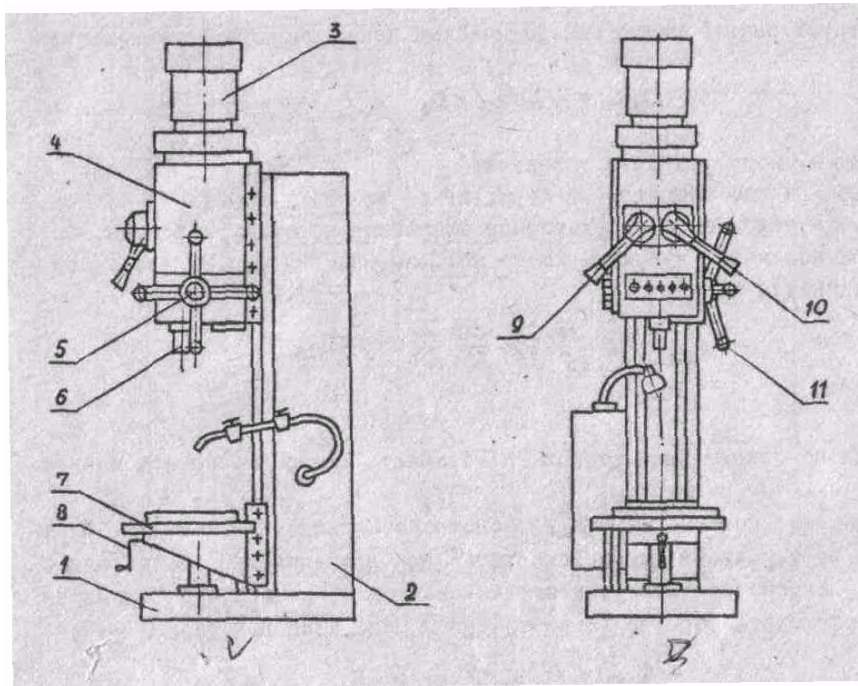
Схема вертикально-свердильного верстату 2Н125
